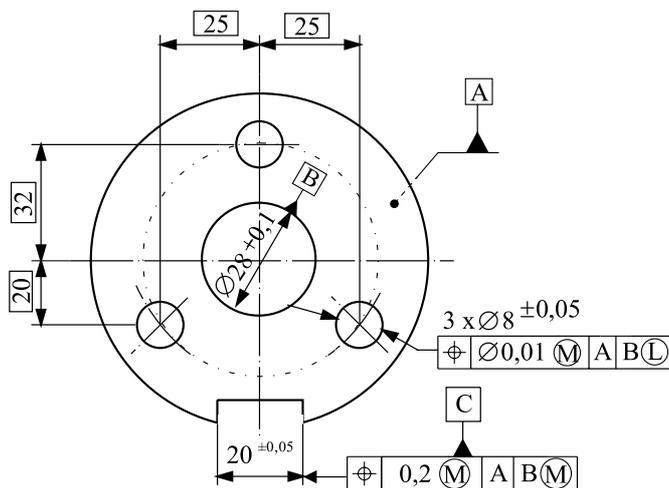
Bauteil mit Ausrichtung der Bezüge
